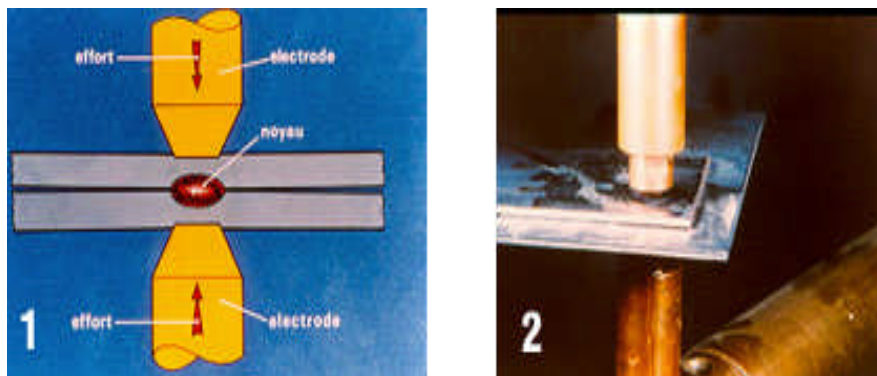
Soudage par points : principe (photo 1)
